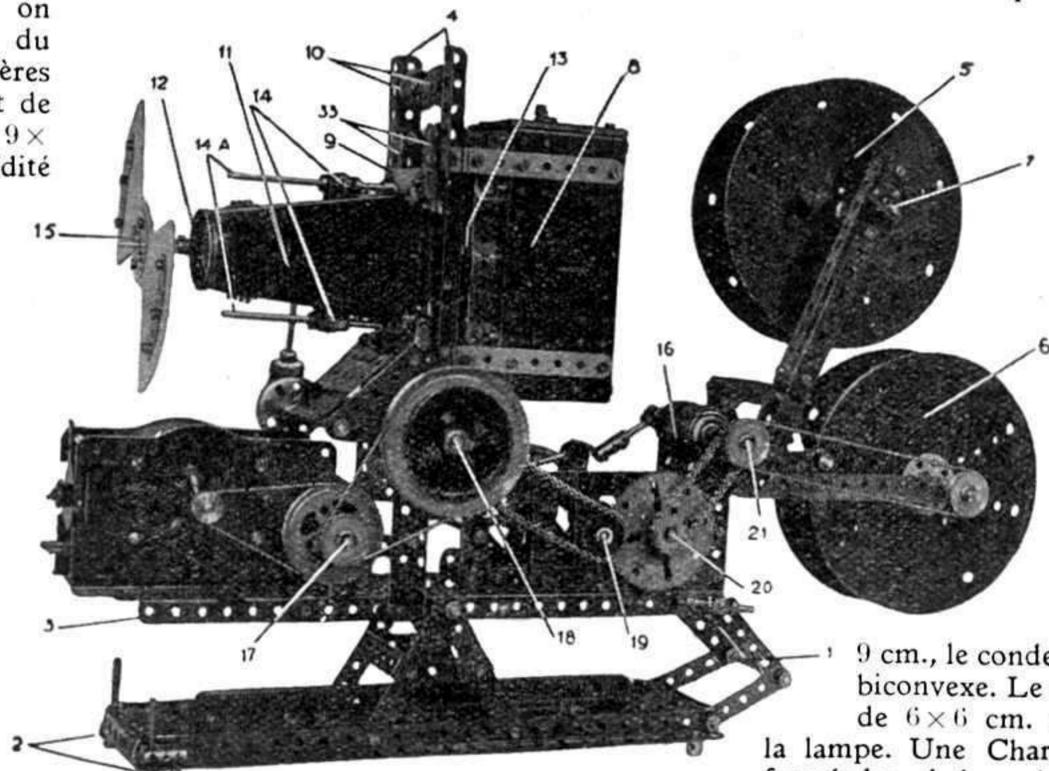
Vue générale de l'appareil de projection cinématographique construit en pièces Meccano.
